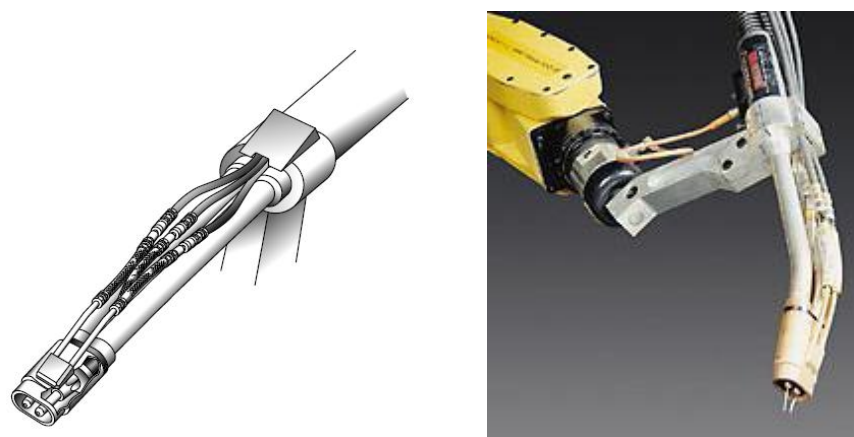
Оборудование для двухэлектродной сварки
